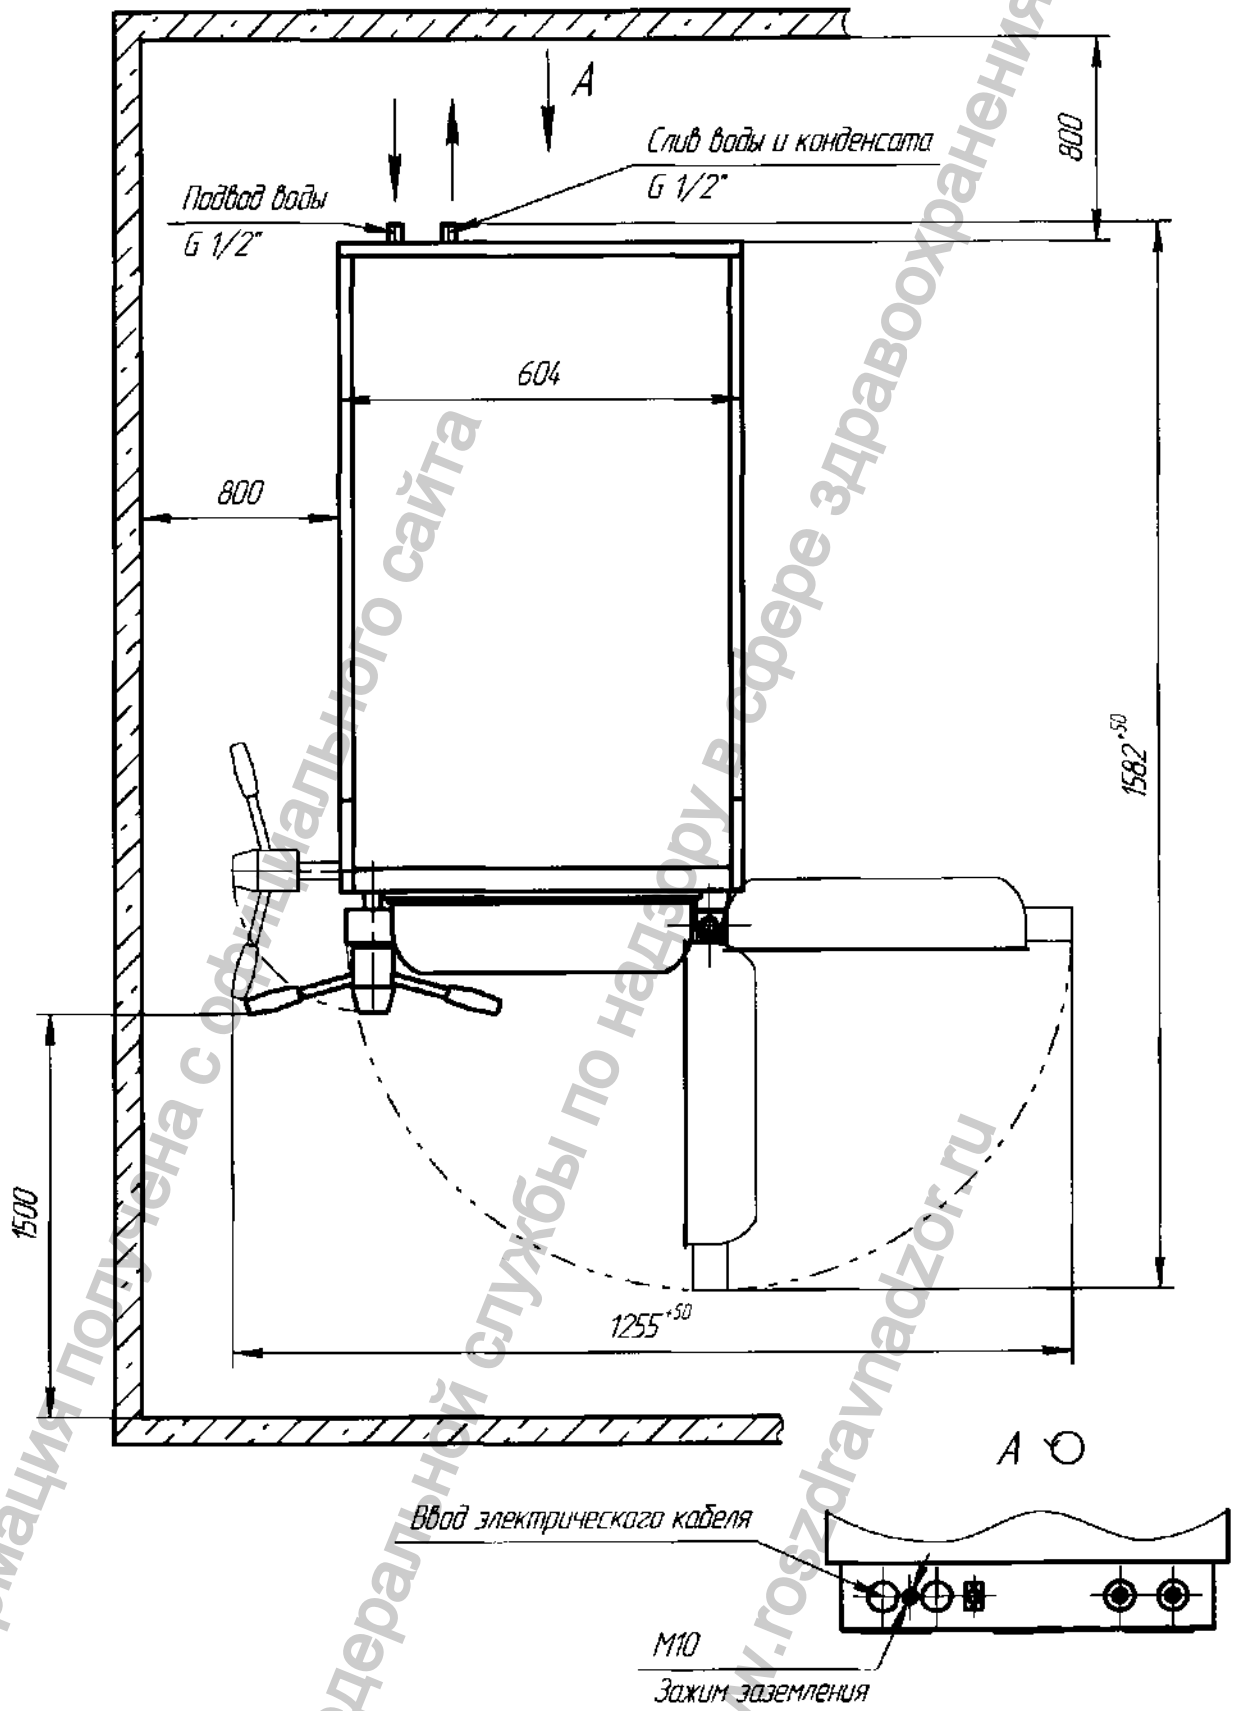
Стерилизатор паровой ГК-100-3. Установочные размеры.
